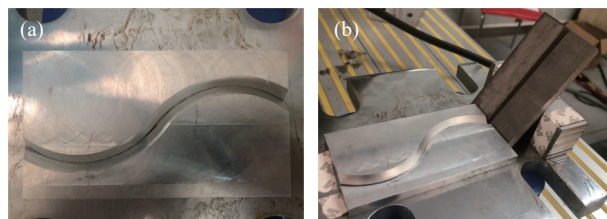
实验对象. (a) S 型焊缝; (b) 三维复杂焊缝
